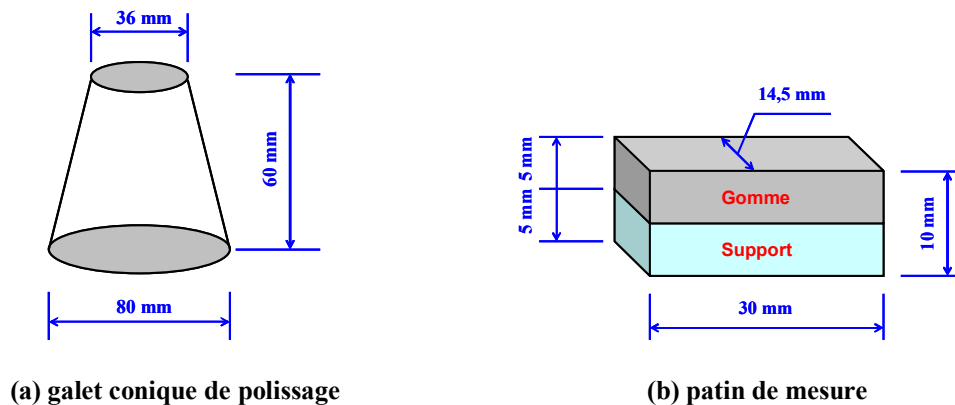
Dimensions de galet conique de polissage et patin de mesure
